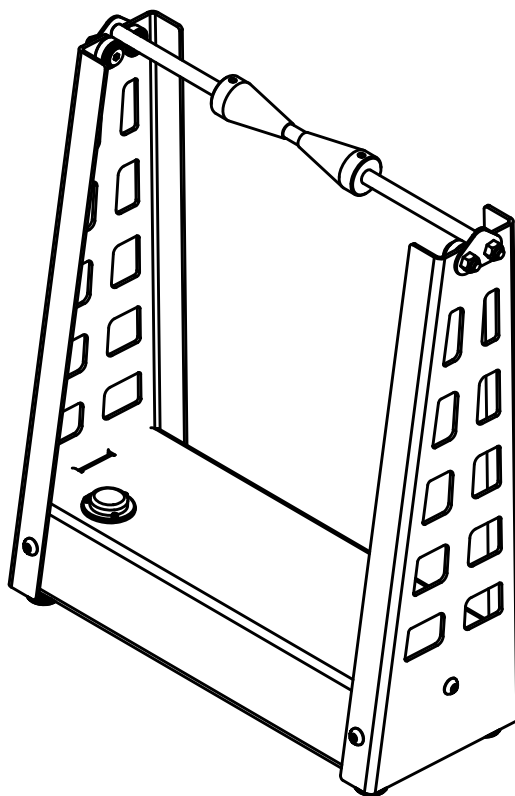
Общий вид собранного стенда для балансировки мотоколес Crazy Iron
